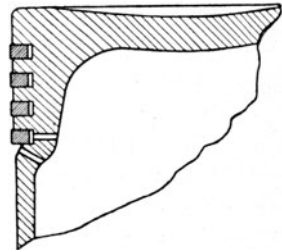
Kolben mit Ölabbaubohrungen am untersten Kolbenring.
